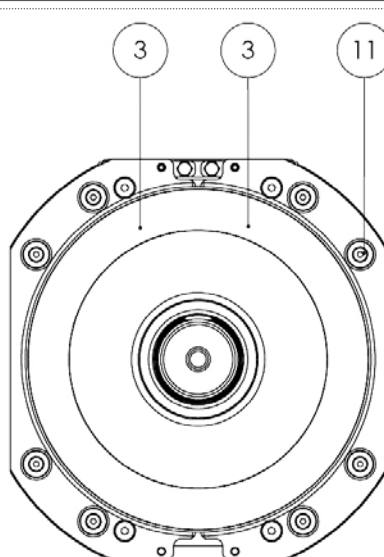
Vue frontale des freins DFX1, DFX2, DFX3 et DF04.
